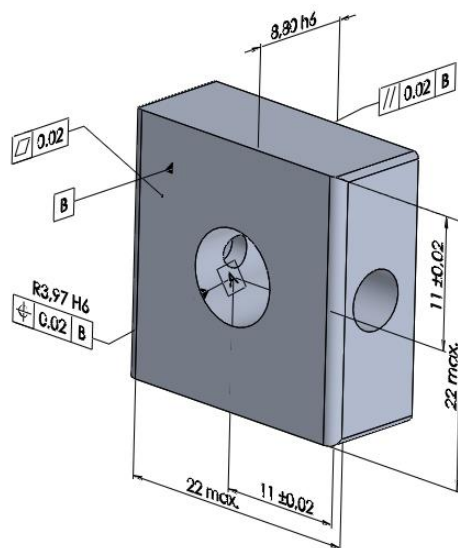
Zadane dimenzijske i geometrijske tolerancije Klizne čeljusti klizača prednjeg uležištenja
